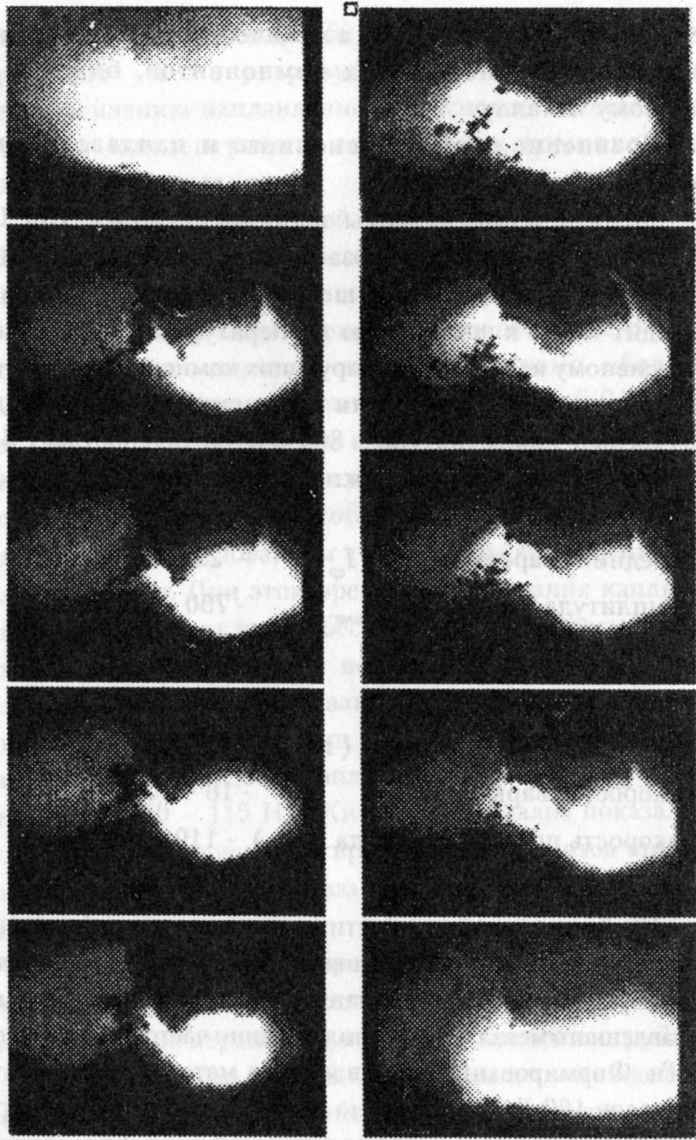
Кинограмма процесса наплавки порошковой проволокой с использованием импульсов сварочного тока частотой 50 Гц
